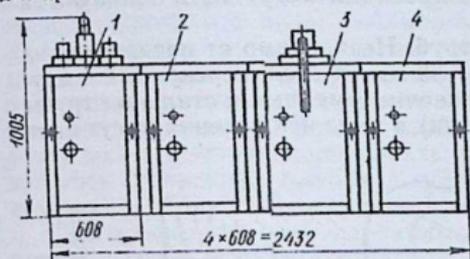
Компонировка контейнеров инструментов, образующих рабочие места для обработки труб (1), сварщика (2), слесаря (3) и электромонтажника (4)
